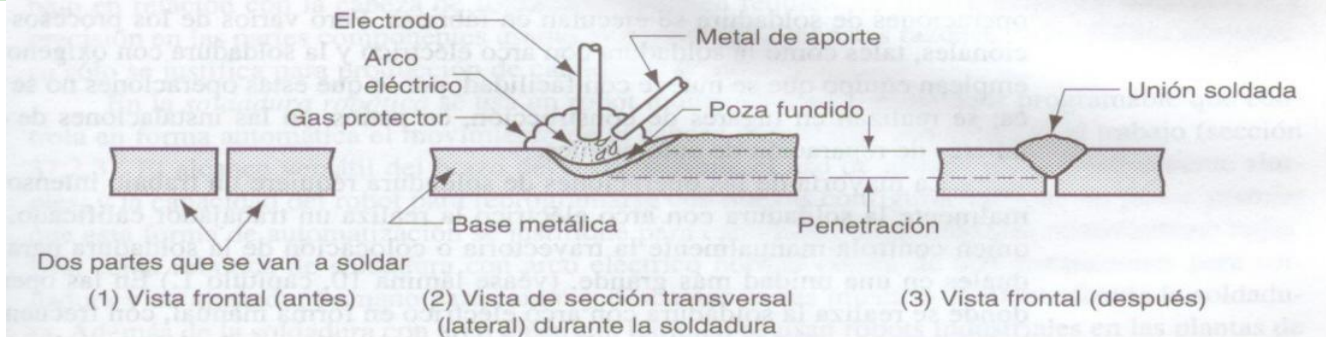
Fundamentos de la soldadura con arco eléctrico: (1) antes de la soldadura; (2) durante la soldadura, se funde la base metálica y se agrega el material de aporte al conjunto fundido y (3) la soldadura terminada.
